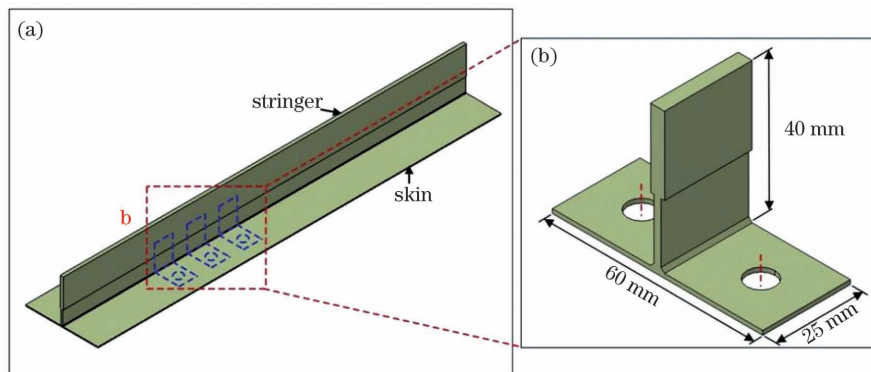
拉伸试样取样位置及尺寸。(a)拉伸试样取样位置;(b)拉伸试样尺寸
